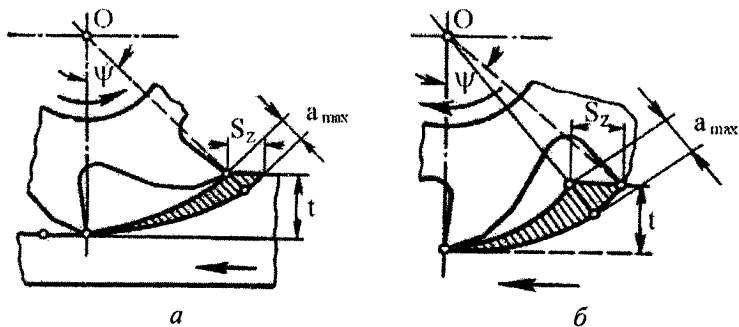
Схеми фрезерування: а – зустрічного; б – попутного
